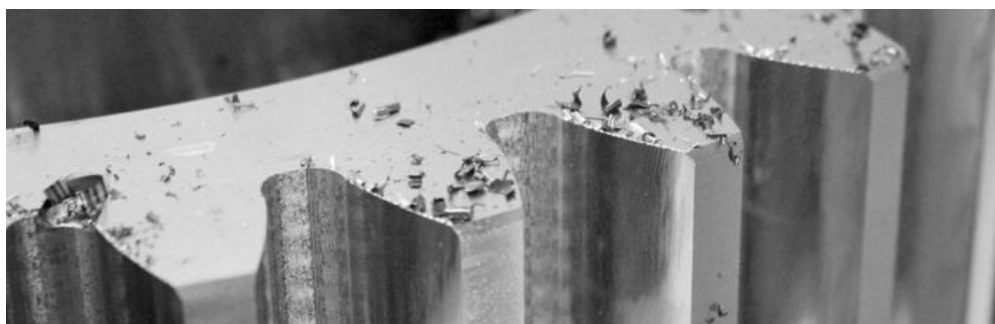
Вид поверхности профиля зуба после фрезерования по технологии Invomilling. На поверхности видны характерные следы в виде «строчек» от траектории движения инструмента
